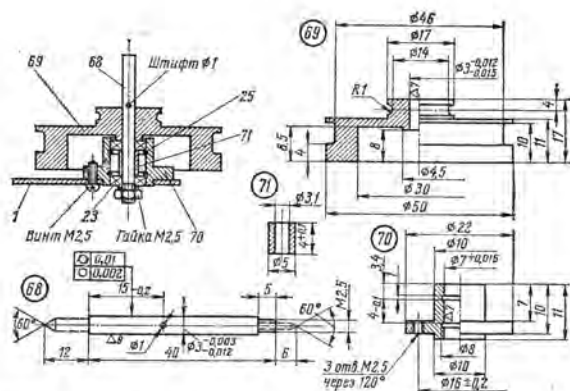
Узел ведущего вала; 1 — шасси; 23 — шариковый подшипник 20000083 ($7 \times 3 \times 2,5$ мм), 2 шт; 25 — кольцо пружинное, 2 шт; 68 — ведущий вал, Ст. 9ХС, калиты ИРС 60...64, шлифовать, 1 шт, запрессовать в детали 69; 69 — маховик, Ст. 20, 1 шт; 70 — втулка, Д16-Т, 1 шт; 71 — кольцо расpornoe, Д16-Т, 1 шт.
